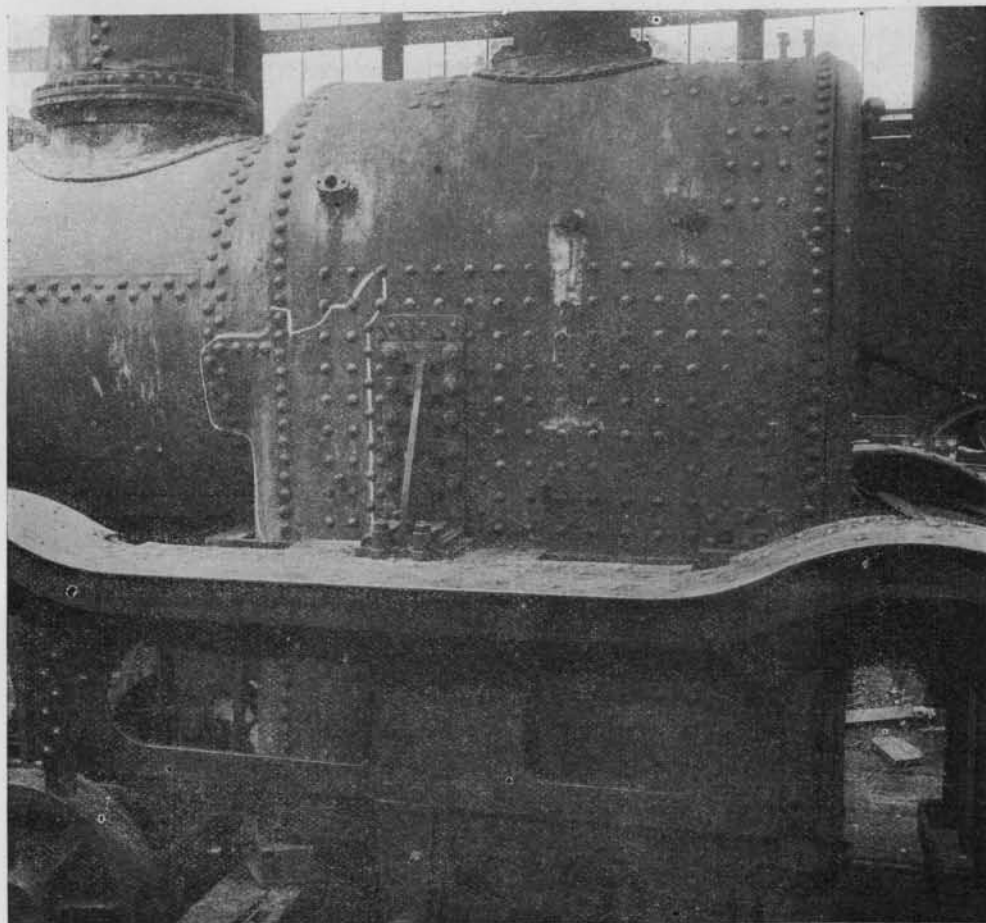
Photographie montrant sur une chaudière de locomotive semblable à celle qui a fait explosion, l'emplacement de l'avarie initiale, au milieu de la hanche et du flanc gauche de la boîte à feu.
